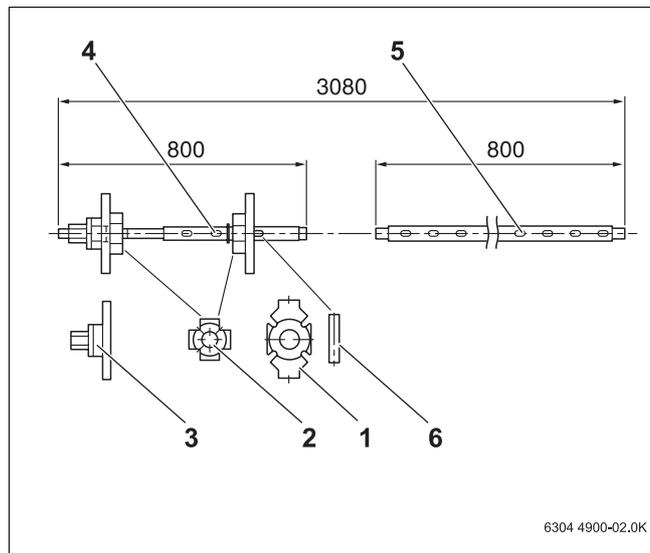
Strettoi di montaggio dimensioni 2.3 (misure in mm)
